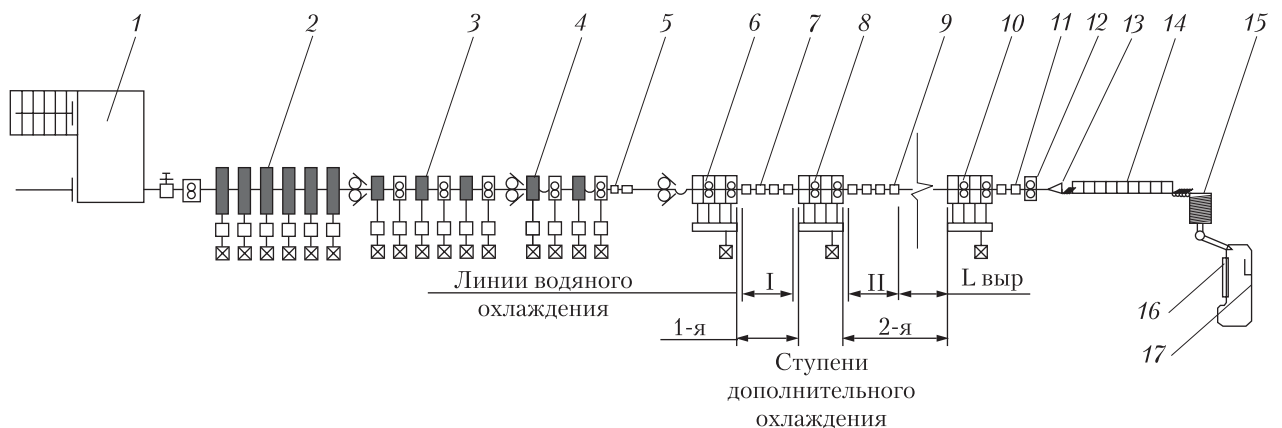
Схема расположения основного технологического оборудования высокоскоростного проволочного стана 150 нового поколения для прокатки катанки широкого размерного и марочного сортамента: 1 — печь с шагающим подом; 2 — черновая группа клетей Н–600; 3 — первая промежуточная группа клетей Н–V 360; 4 — вторая промежуточная группа клетей Н–V 330; 5 — секция предварительного водяного охлаждения раската; 6 — первый миниблок 215–190; 7 — первая линия дополнительного водяного охлаждения раската; 8 — второй миниблок 170–150; 9 — вторая линия дополнительного водяного охлаждения раската; 10 — редуционно-калибрующий миниблок 205–230; 11 — линия окончательного водяного охлаждения катанки; 12 — трайбаппарат; 13 — виткообразователь; 14 — роликовый транспортер с крышками для воздушного охлаждения катанки; 15 — виткосборник; 16 — пресс и инспекторский стеллаж; 17 — крюковой конвейер
